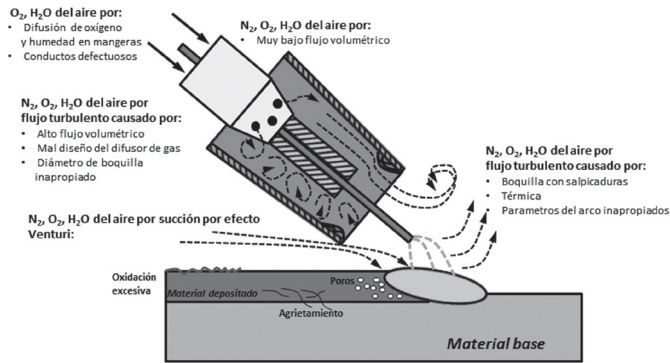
Esquema de fuentes de contaminación del gas de protección y defectos de soldadura.
